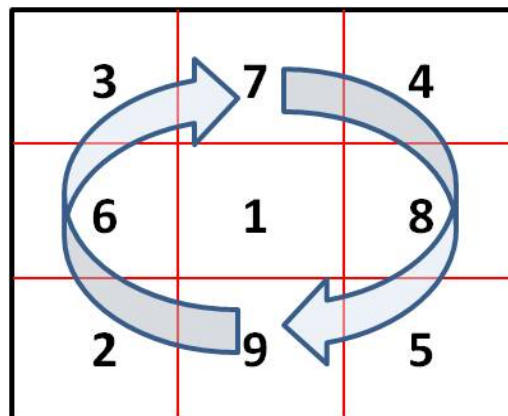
Sequência de soldagem realizada durante o ensaio.
